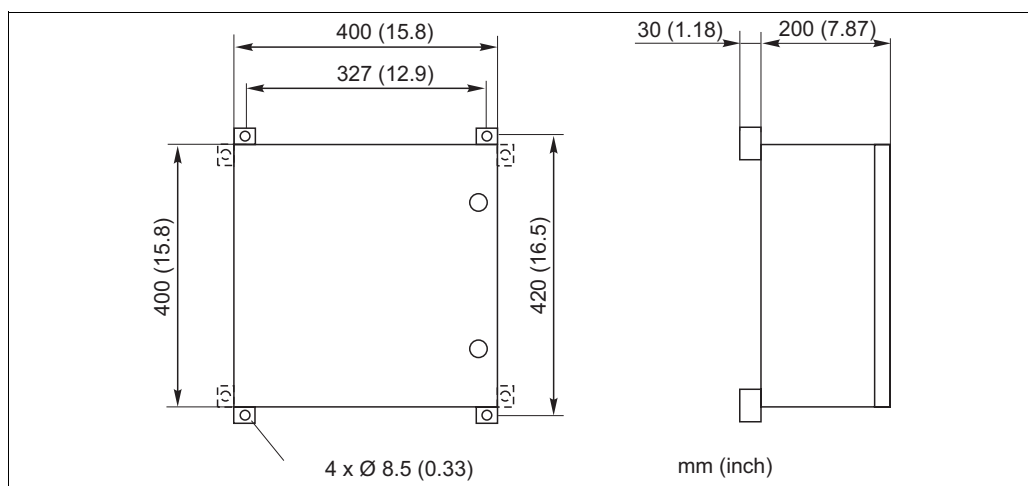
Dimensioni della scatola di controllo, vista frontale sinistra, vista laterale destra
